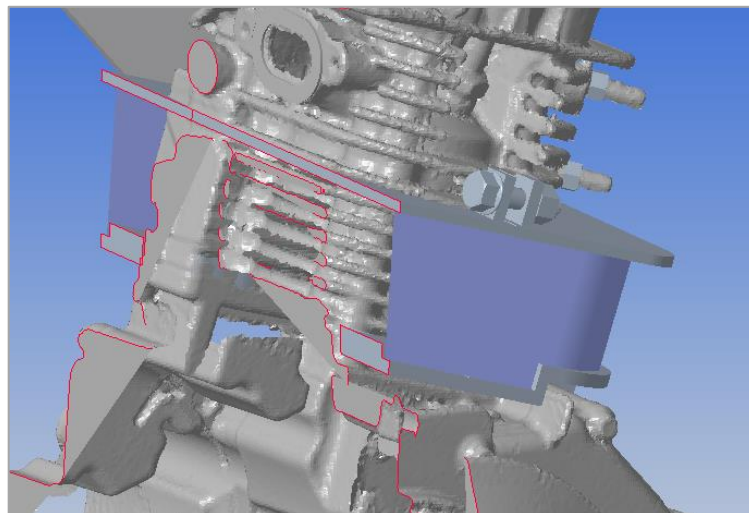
Zusammenbau des Kühlmantels mit dem Zylinder
